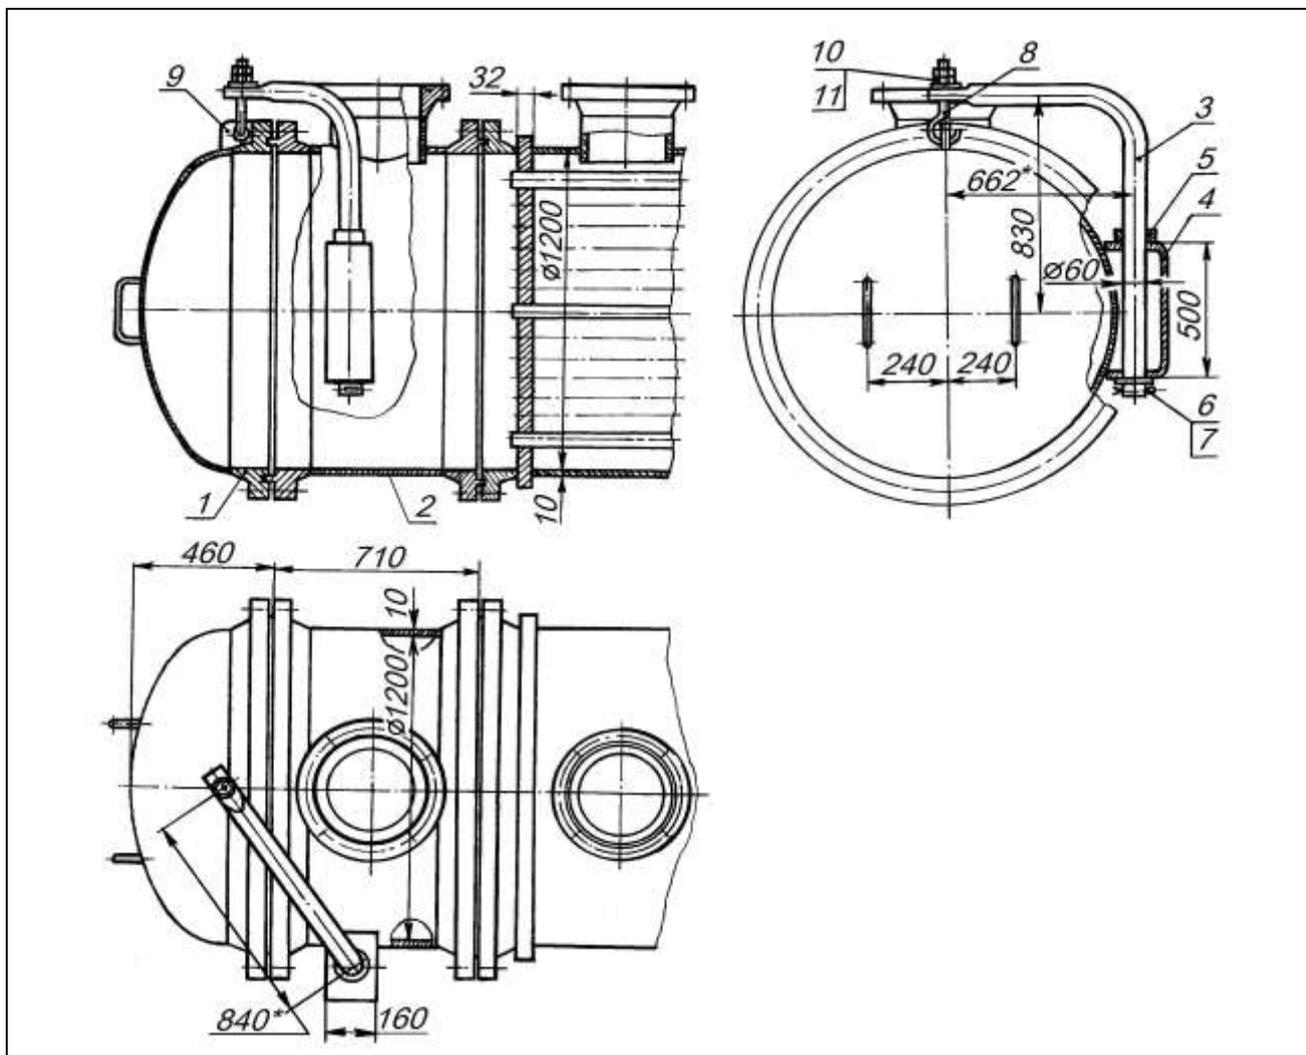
Поворотно-удерживающее устройство для крышки 1 распределительной камеры 2 горизонтального теплообменника: 3 – кронштейн; 4 – изогнутая пластина для установки кронштейна; 5 – опорное кольцо; 6 – шайба; 7 – шплинт; 8 – крюк с резьбой М16; 9 – ушко; 10 – гайка; 11 – контргайка
